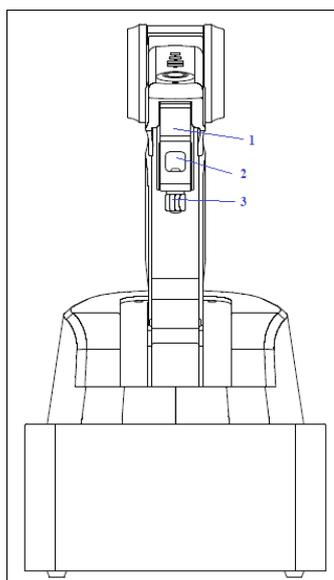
Манипулятор (вид спереди), где 1 – блок инструмента; 2 – гнездо фиксатора блока инструмента; 3 – прижимной винт
